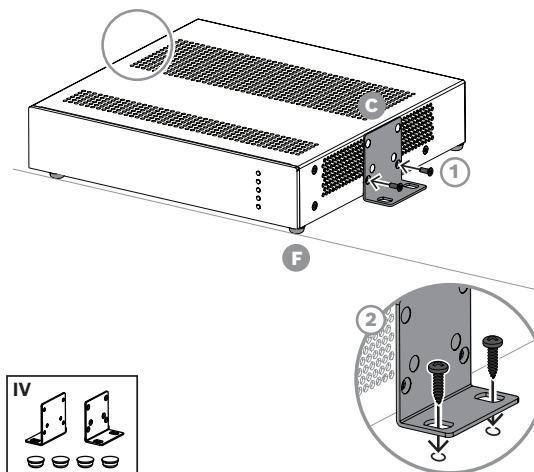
Настольное использование: монтаж над столом (U120:1/U240:1)
